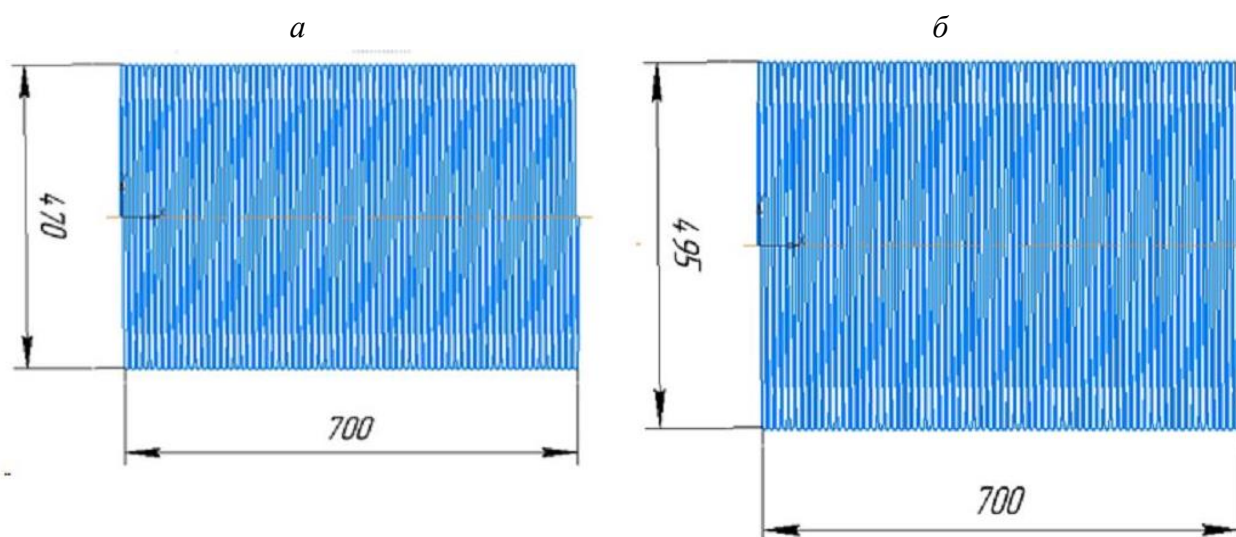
Габаритные размеры обмотки сглаживающего реактора: штатная (а) и модернизированная (б)
